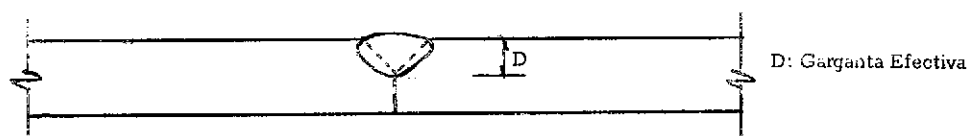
Soldadura de bisel de penetración parcial.
